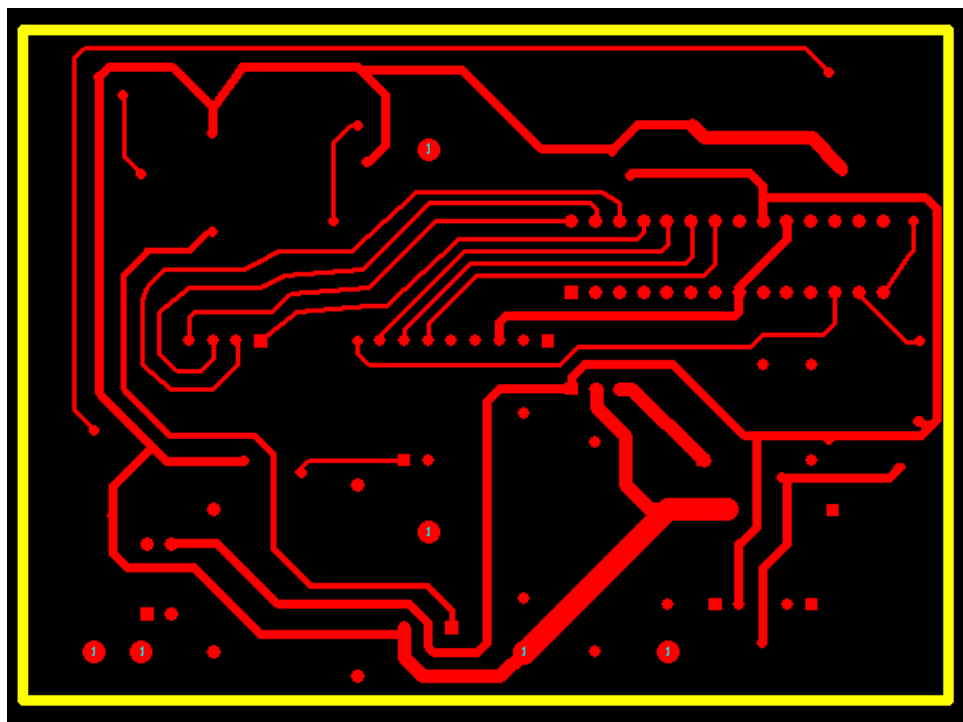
Tarjeta electrónica del metro contador, cara de soldadura.
